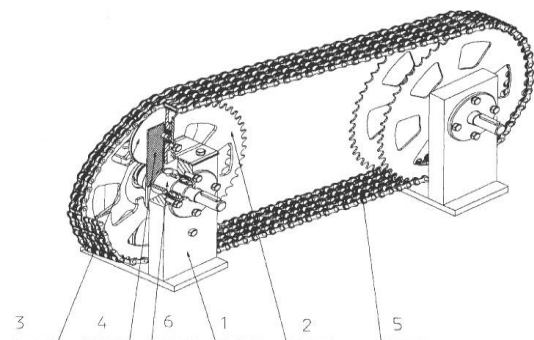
Хвильова ланцюгова передача: 1 - корпус; 2 - нерухома зірочка; 3 - катки; 4 - водило; 5 - ланцюг; 6 - приводний вал
